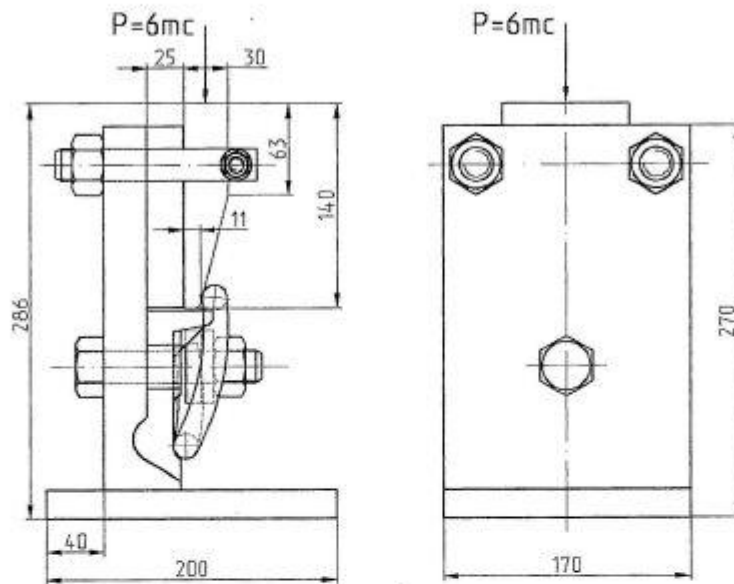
Схема испытания упора на боковую нагрузку
